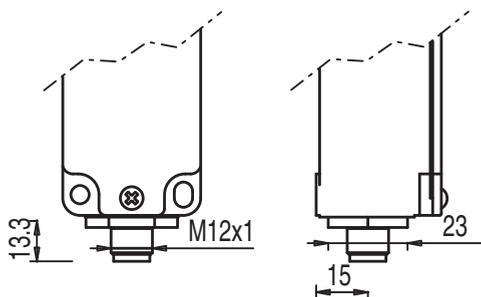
Dimensioni S200-M4C1-M12 in mm (qui dimensioni connettore M12)
